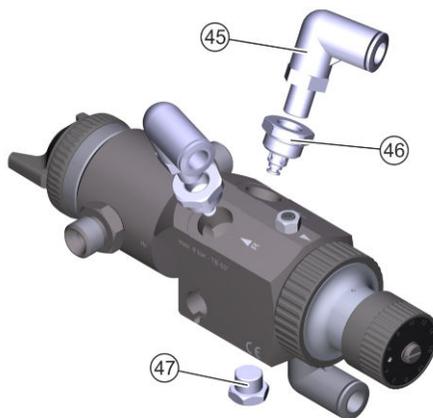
Vista detallada accesorios del robot (variante pistola de inyección RC)
